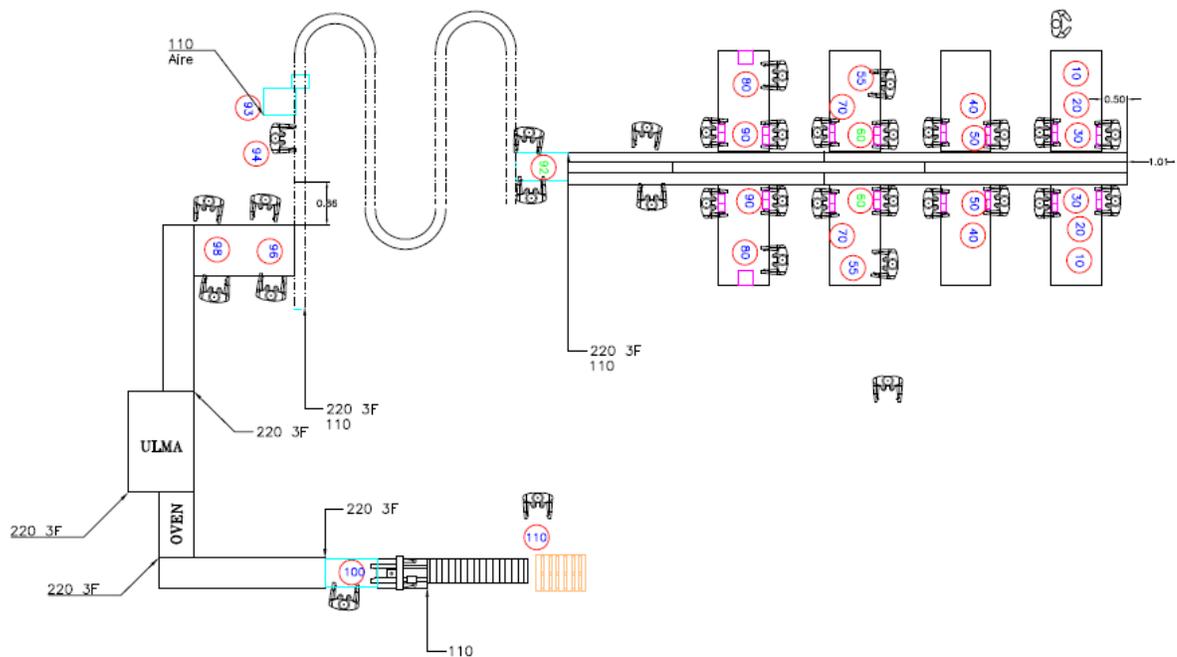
Línea de manufactura acoplada (ASMD, 2017)
